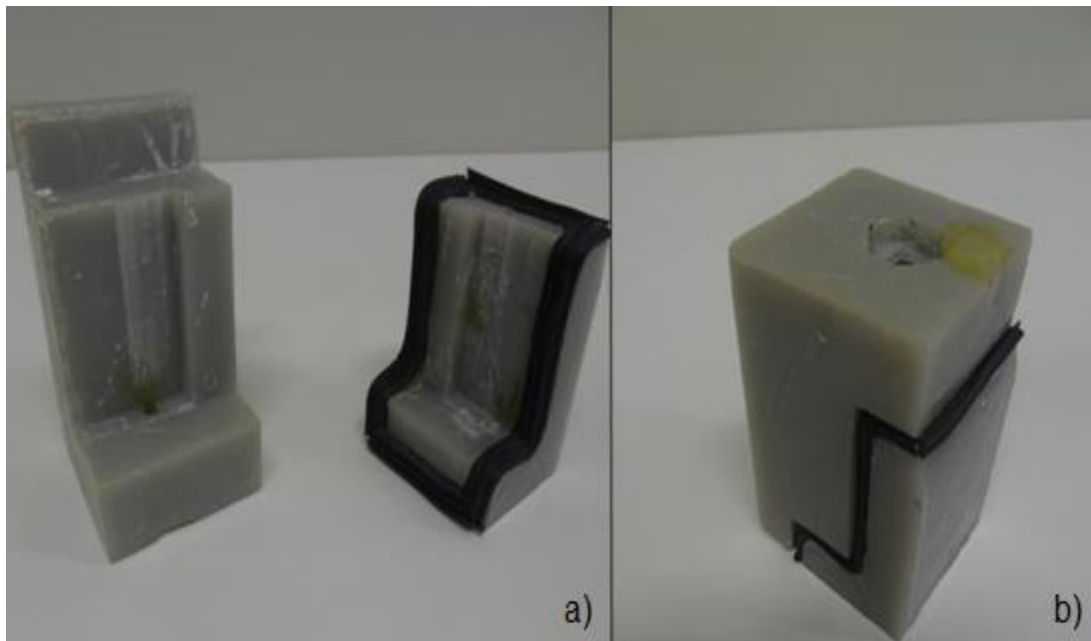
Molde em Epóxi para a injeção: a) Molde aberto e b) molde fechado
